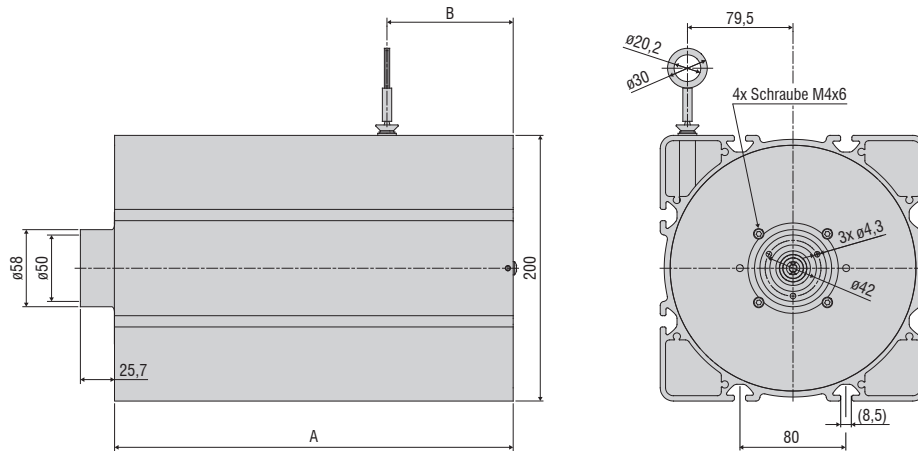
Maßzeichnung WDS- ... - P200 - XX - XXX, Abmessungen in mm
